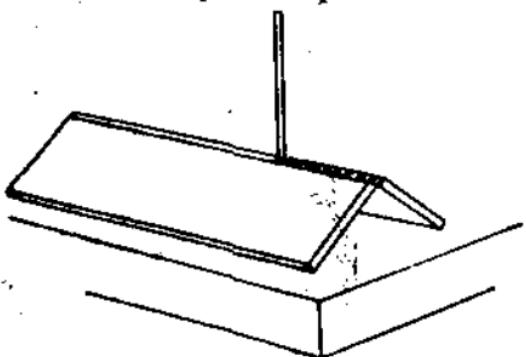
Положение пластины для сварки в уроке 11.
